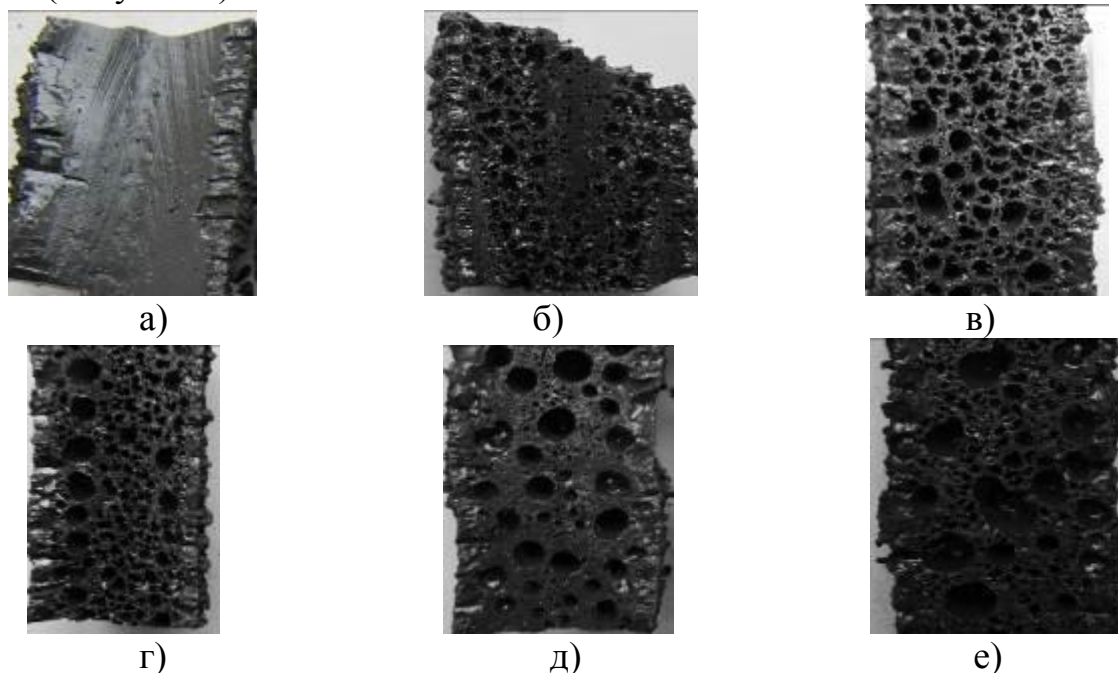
Вид шлаковой корки со стороны сварного шва
